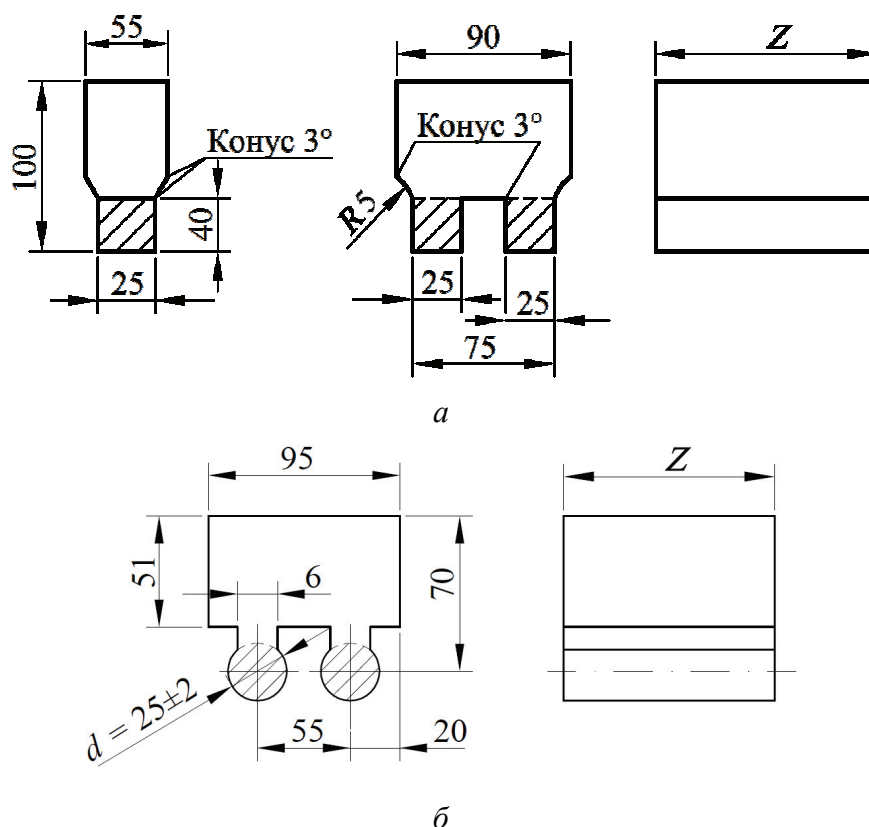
Форма и размеры литых заготовок для изготовления образцов с различной формой сечения: а – прямоугольная; б – круглая; Z выбирается в зависимости от размера и количества образцов. Заштрихованные участки соответствуют месту вырезки образцов
